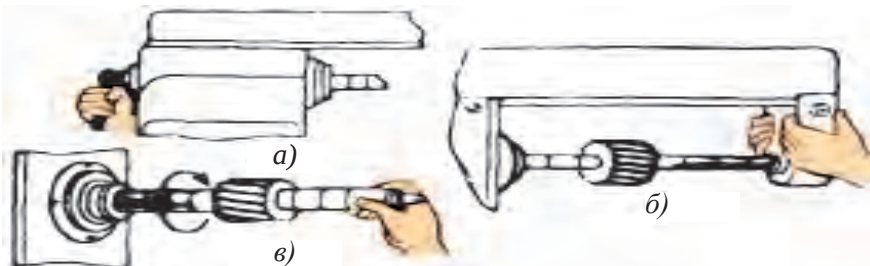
Установка цилиндрической фрезы: а – установка оправки; б – размещение установочного кольца; в – установка фрезы.
